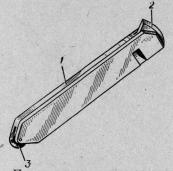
1 — корпус; 2 — нож; 3 — ролик
